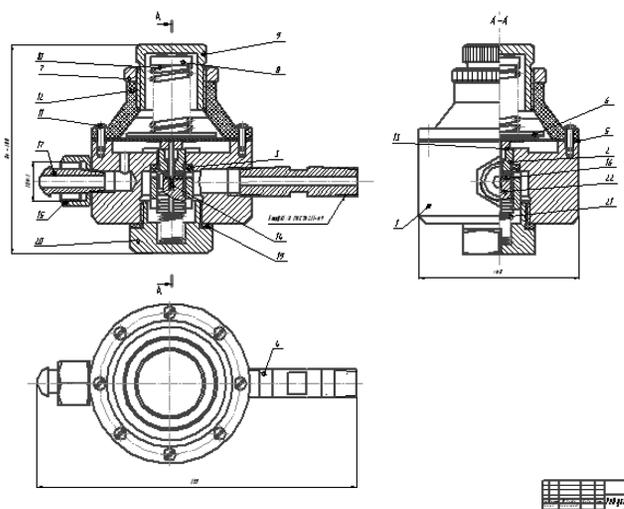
Выполнение сборочного чертежа по чертежам деталей
